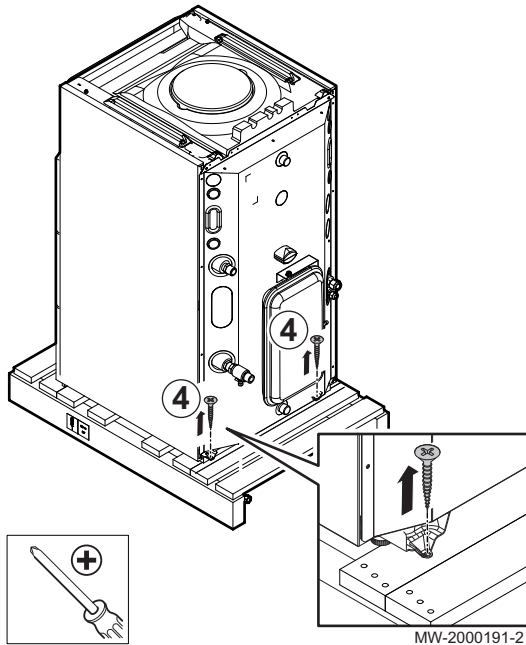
Die Befestigungsschrauben an der Rückseite entfernen
